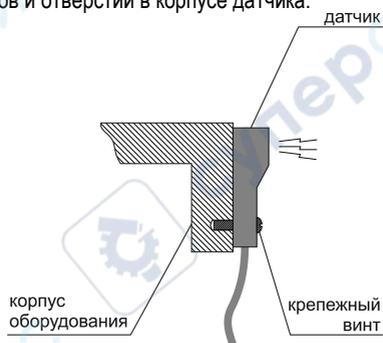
Установка датчика с торцевым расположением чувствительной поверхности
